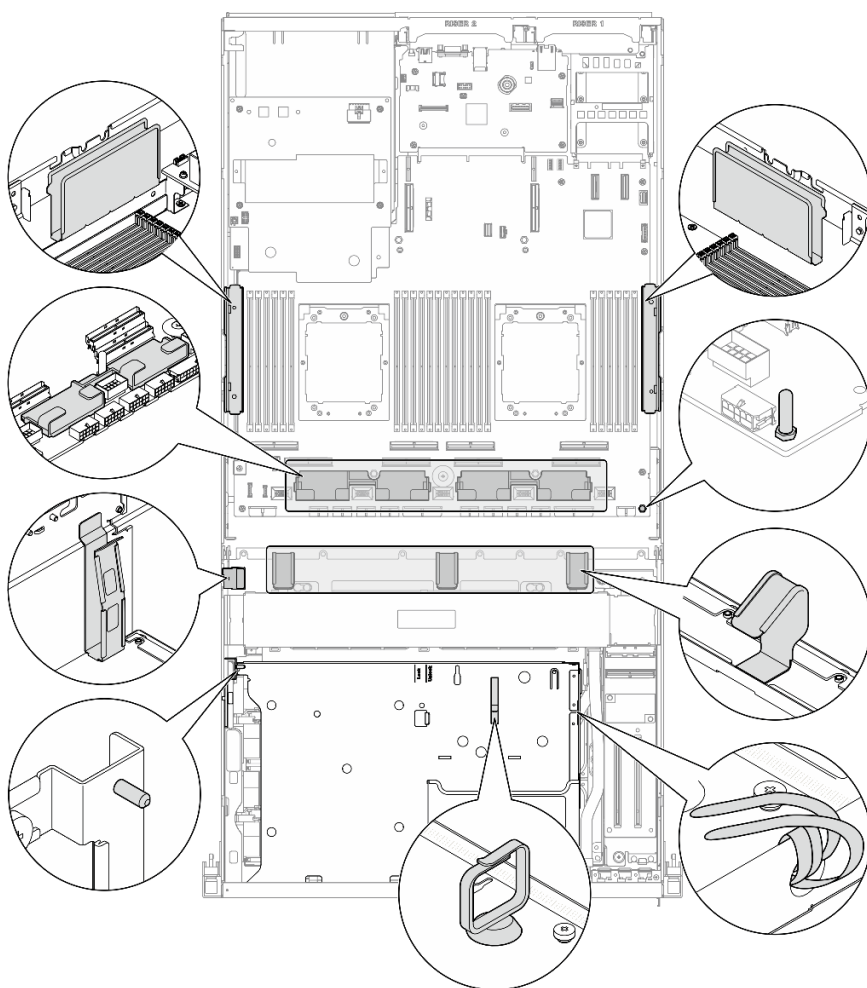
Guía de cables, clip de cables, guía de sujeción de cables y ubicaciones de bridas para cables en el chasis
